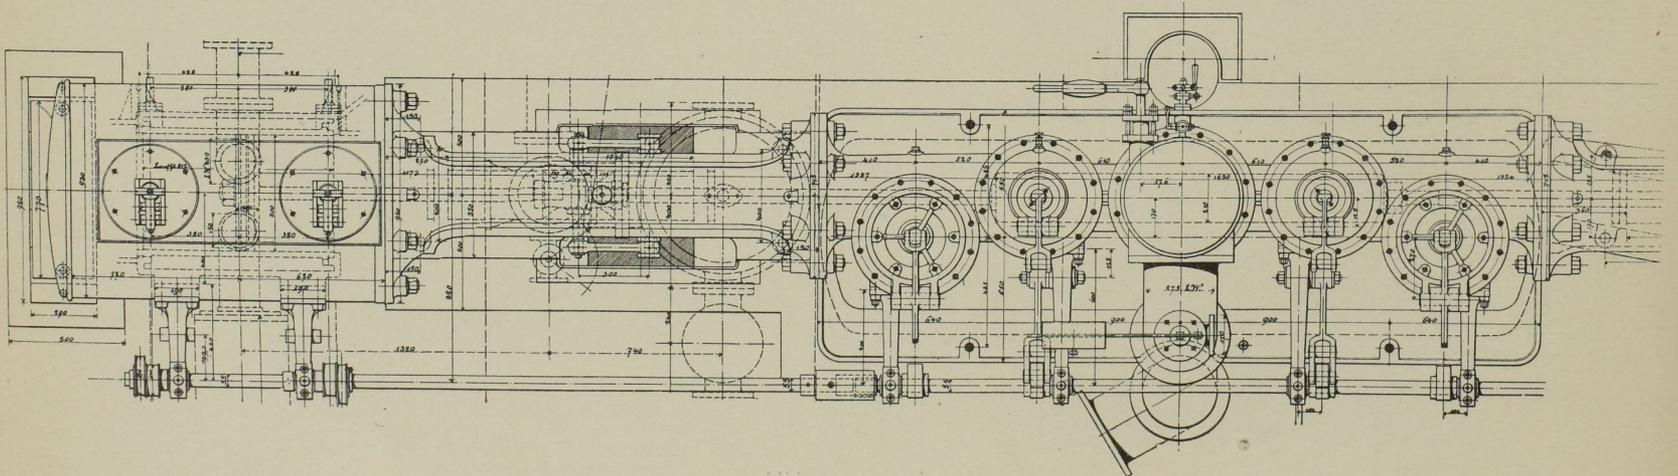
Grundriss der Druckpumpe. Massst. 1:30.
